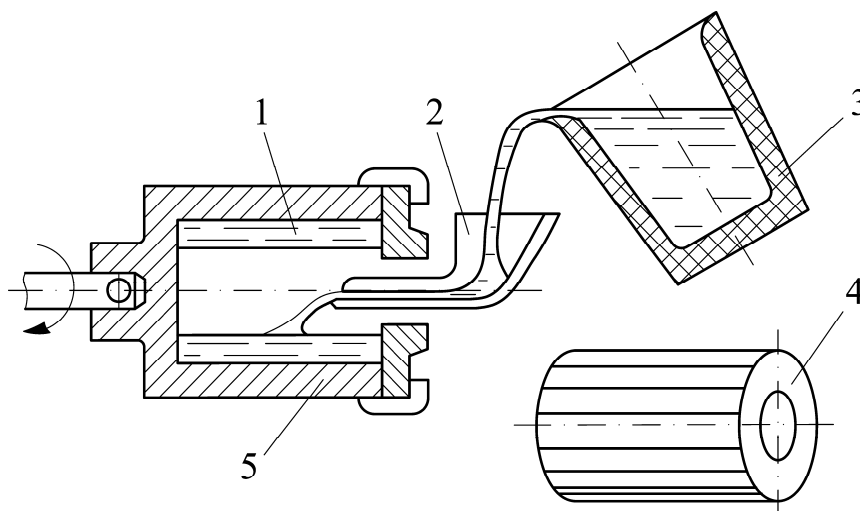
Схема получения отливки при вращении формы вокруг горизонтальной оси: 1 – расплав; 2 – заливочный желоб; 3 – ковш; 4 – отливка; 5 – форма
